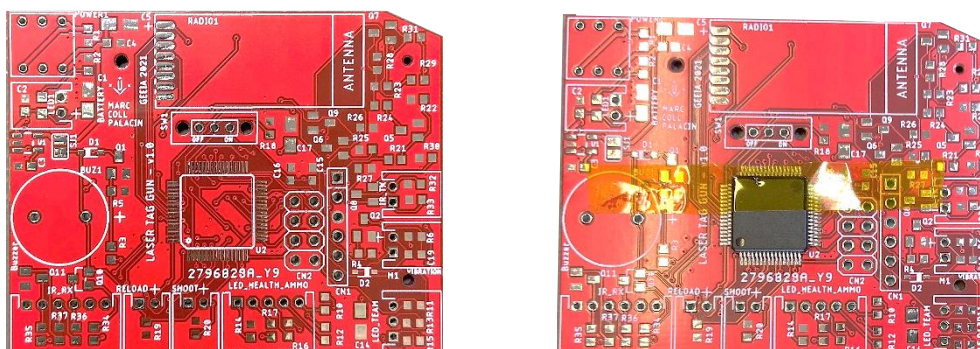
Cara posterior de la PCB neta i MCU presoldat
